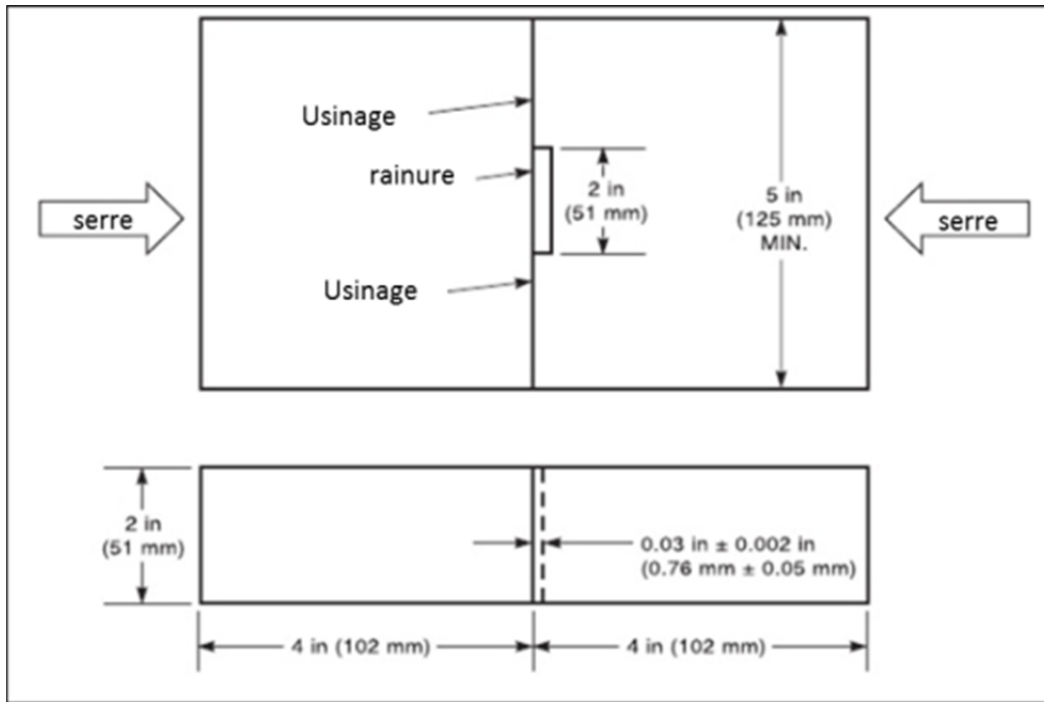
Éprouvette GBOP tirée de (American Welding Society, 2007)
